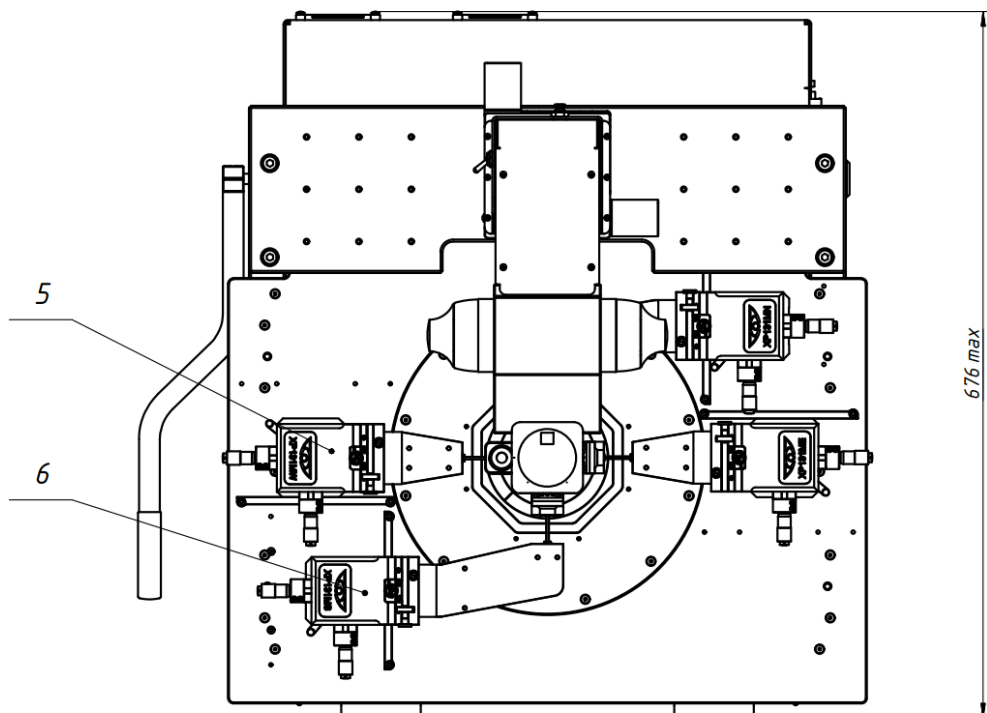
Габаритный чертёж полуавтоматической зондовой станции Terra-200COAX вид
